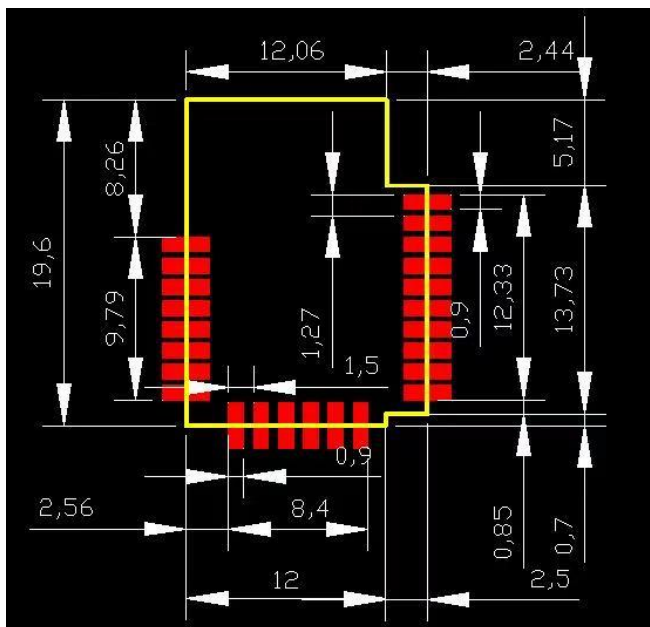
物理尺寸及推荐占地面积(单位:mm, 偏差:0.02mm)
